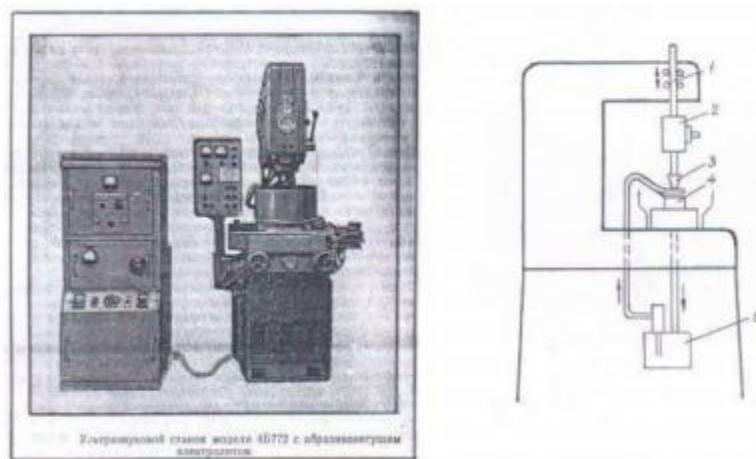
Основные узлы ультразвукового станка. 1 – механизм подачи головки; 2 – акустическая головка; 3 – стол со сменными ваннами; 5 – система подвода и отвода абразивной суспензии
